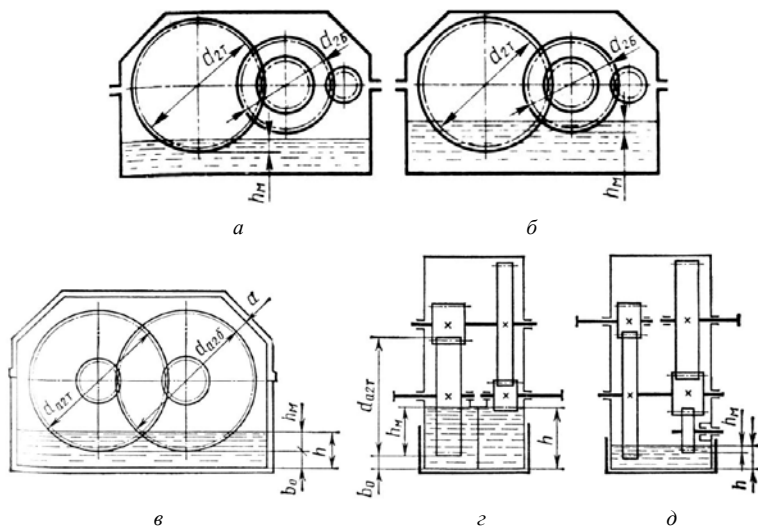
Глубина погружения в масло деталей цилиндрического редуктора
